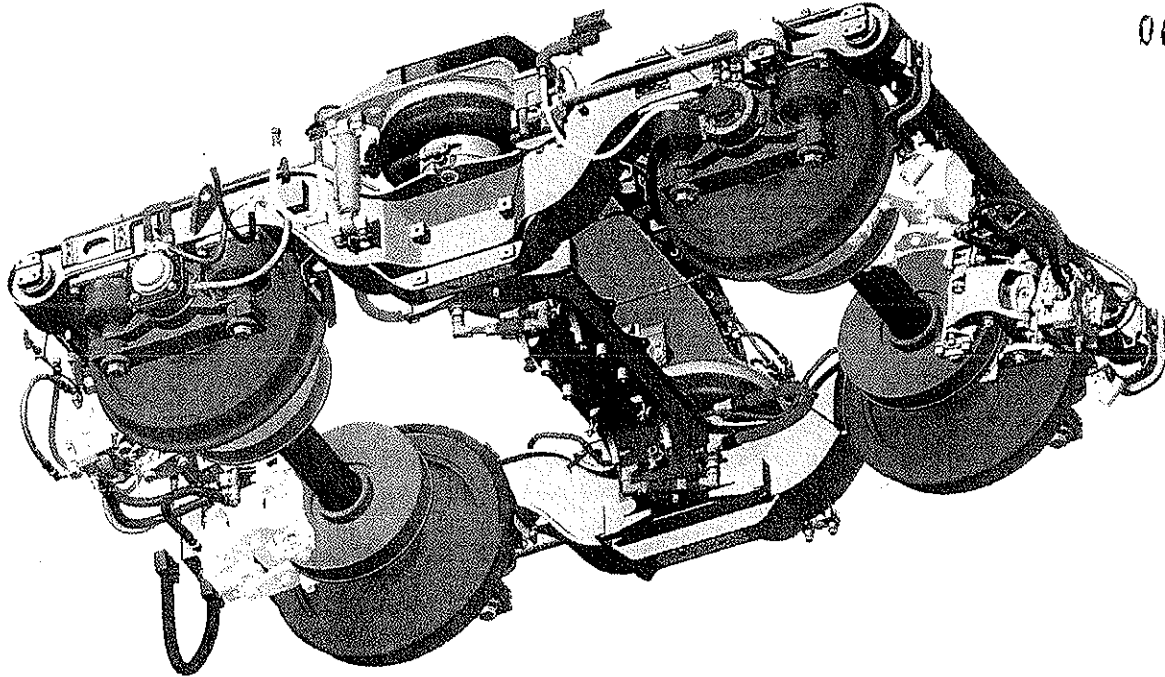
Vista isométrica de la parte inferior del bogie remolque
